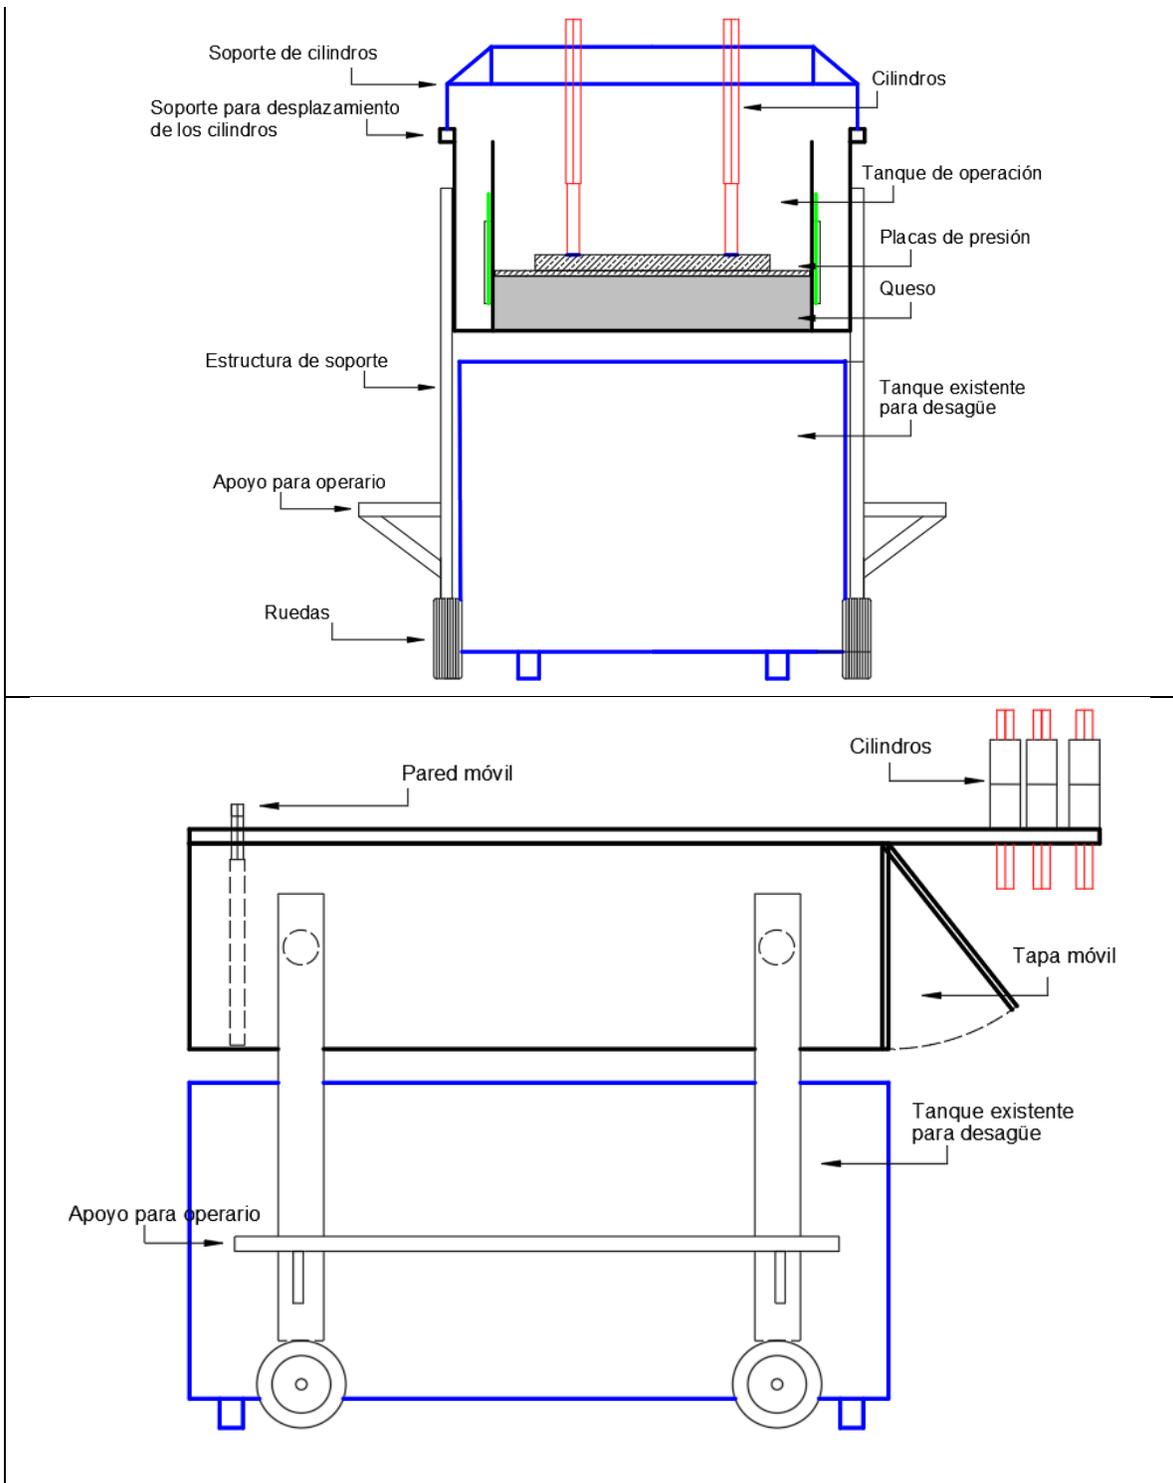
Dibujos de ingeniería de detalles, sección transversal y vista lateral del prototipo completo.
